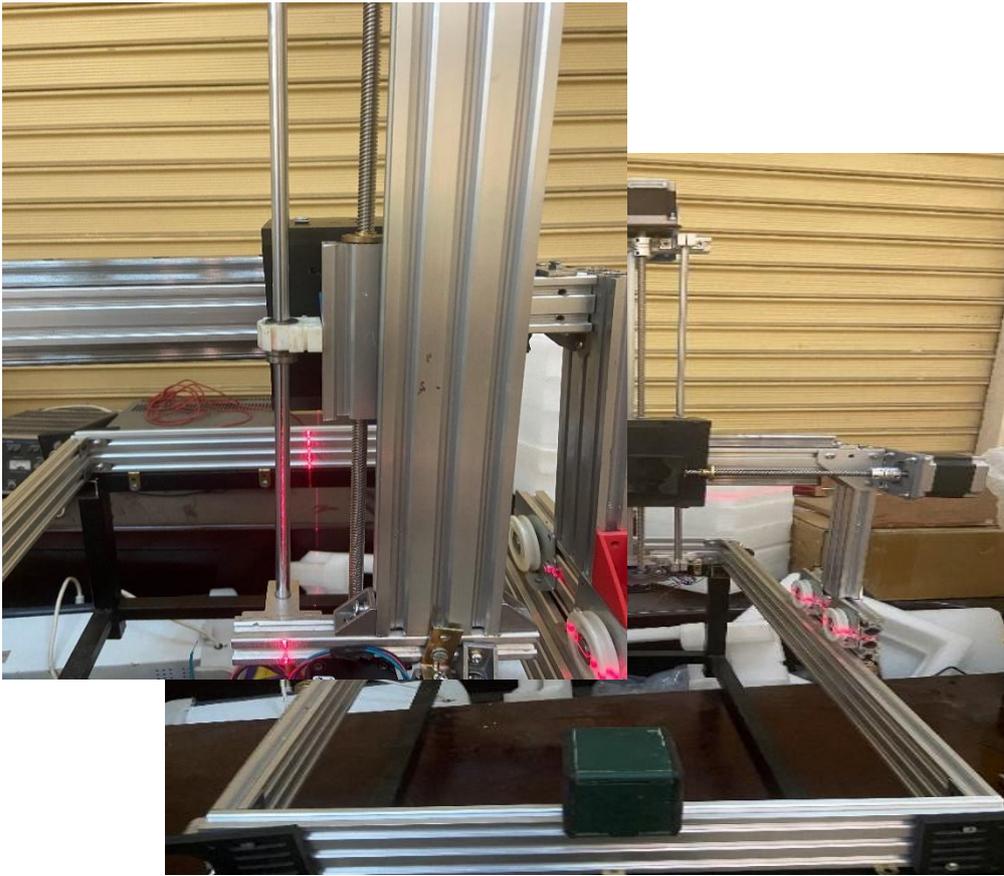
vérification de l'Assemblage de la machine à l'aide du Laser Tracker
